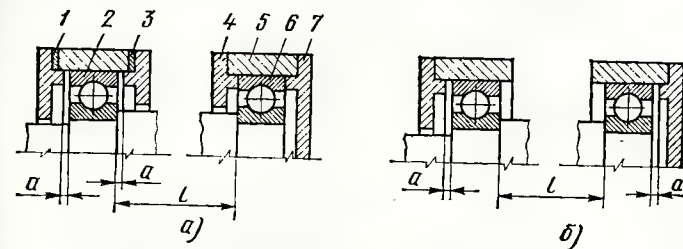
Установка шарикоподшипников: а — с фиксированной опорой, б — враспор; l — расстояние между подшипниками, a — зазор между фланцем и подшипником
